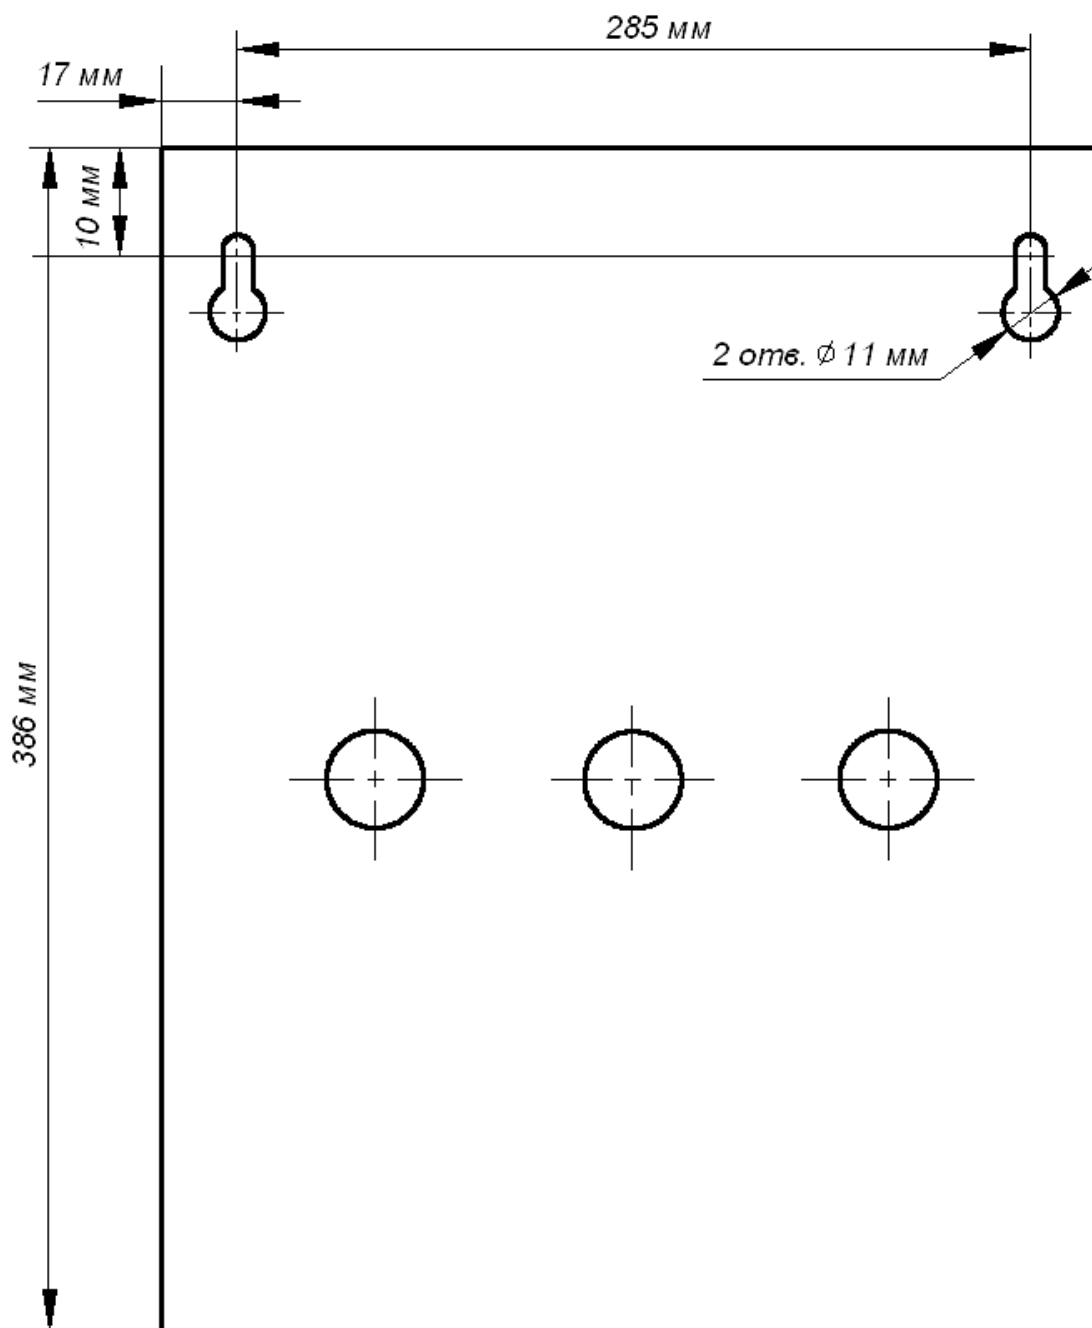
Установочный чертеж прибора «А16-512» (корпус выпускался до 2012 года)
